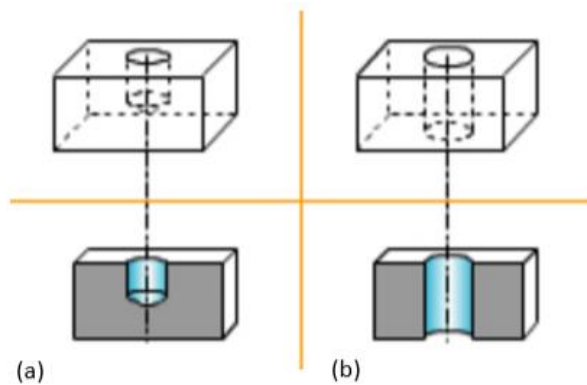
(a) Barreno ciego: El barreno no tiene salida al lado opuesto de la pieza. (b) Barreno pasado: El barreno pasa al lado opuesto de la pieza. [16]
